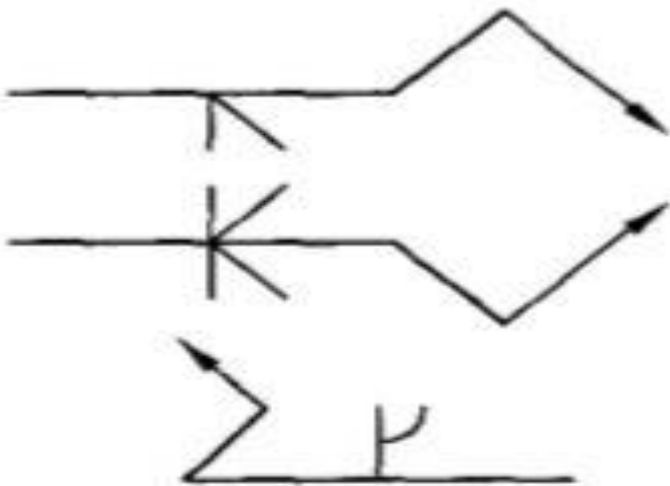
Aplicaciones del Quiebre de la Flecha en el Símbolo de Soldadura
